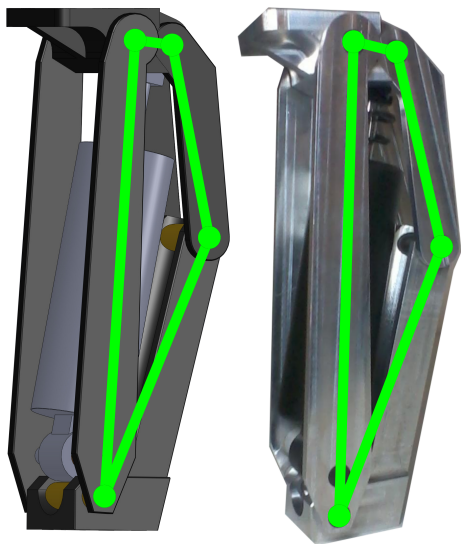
Desenho CAD e protótipo real do mecanismo do joelho com destaque para as barras em verde
